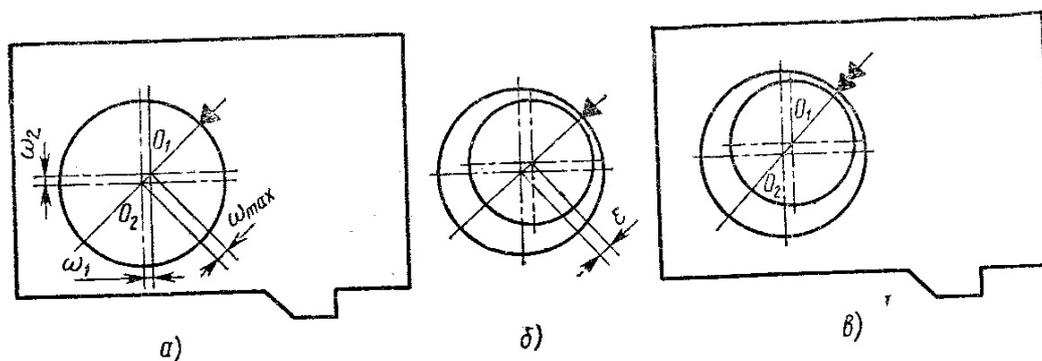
Уменьшение погрешности поворота оси вращения вала относительно основных баз корпуса
